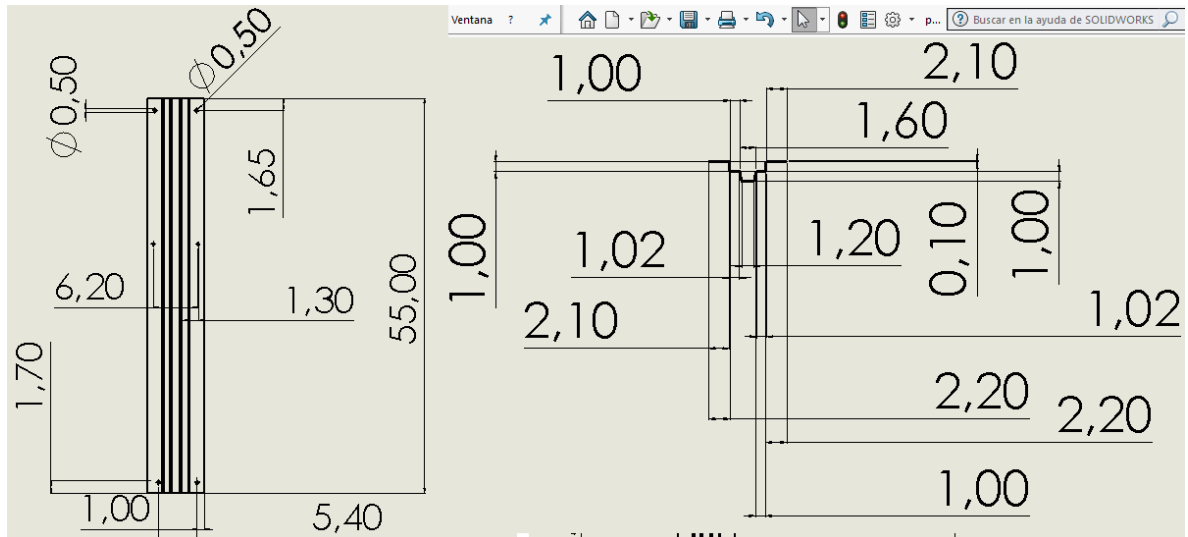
Medidas perfil de acero inoxidable. Autoría propia
